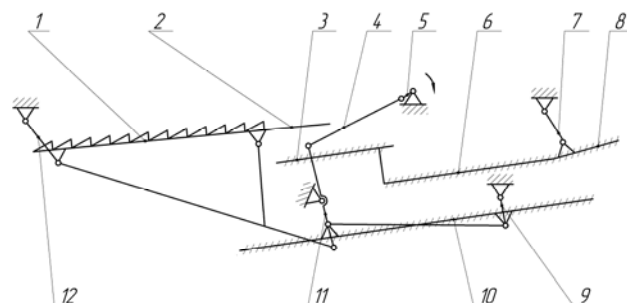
Схема серийной очистки зерноуборочного комплекса «Полесье-Ротор»: 1 – стрясная доска; 2 – пальцевая решетка; 3 – дополнительное решето; 4 – шатун; 5 – кривошип; 6 – верхнее решето; 7, 9, 12 – шарнирные подвески; 8 – удлинитель верхнего решета; 10 – нижнее решето; 11 – двухплечий рычаг
